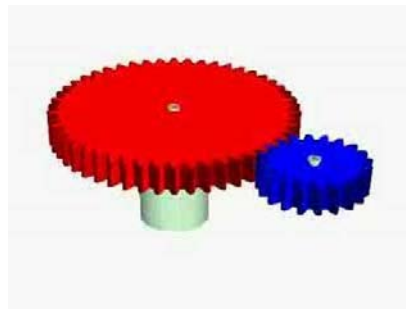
"Gráfico multiplicador de engranajes"
